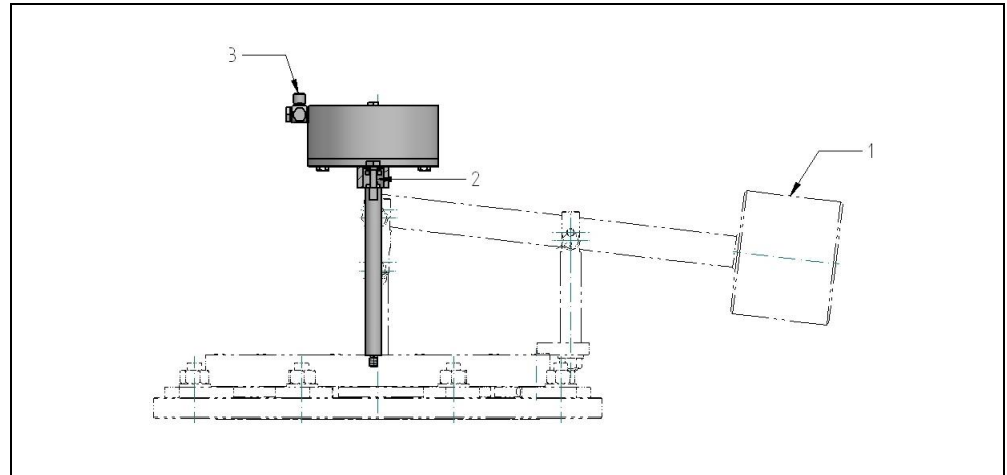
Esquema con dispositivo de levantamiento DN 300 – DN 400
